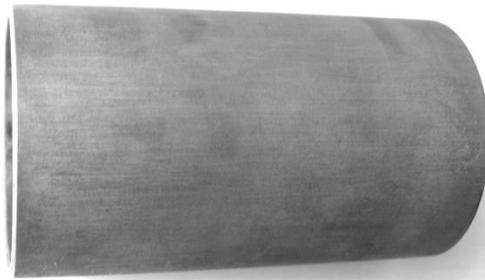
Общий вид образца с наружной поверхностью, подготовленной для электрогальванического осаждения с послойным упрочнением
